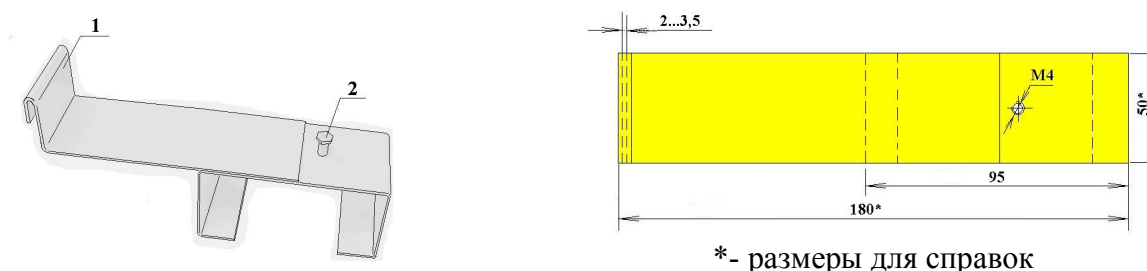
Внешний вид и габаритные размеры кронштейна крепления «БОС» к МПП «Гарант-12»
